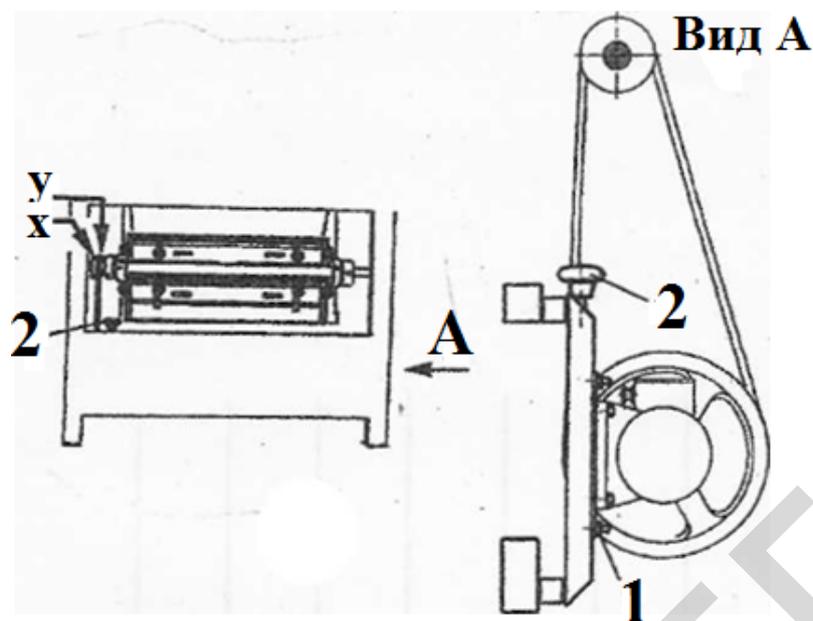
Регулировка оборотов эксцентрикового вала:
